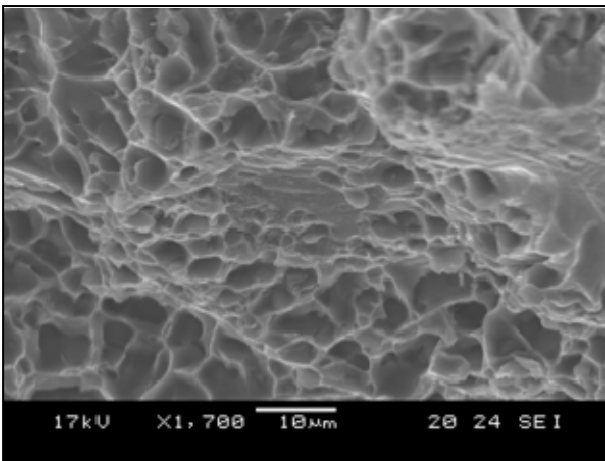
Superficie de fractura del material A356 T6 (SLC).
